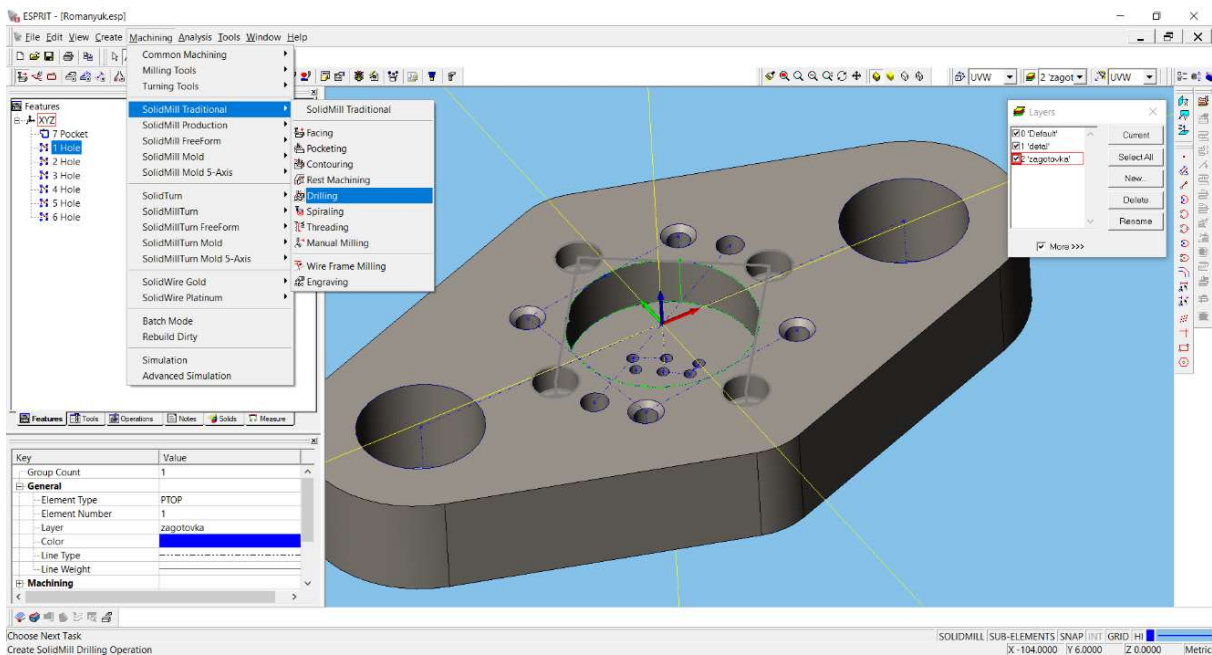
Вибір виду оброблення деталі кришка
